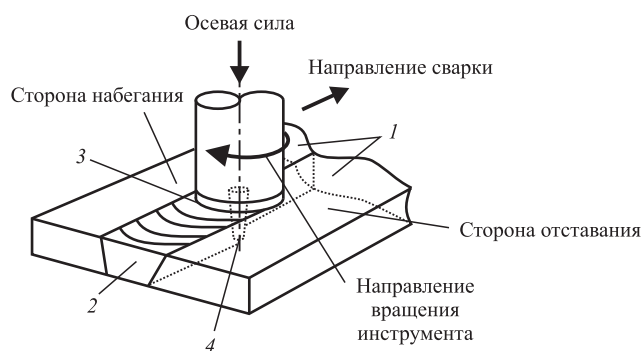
Схема процесса сварки трением с перемешиванием исследуемых сплавов:
